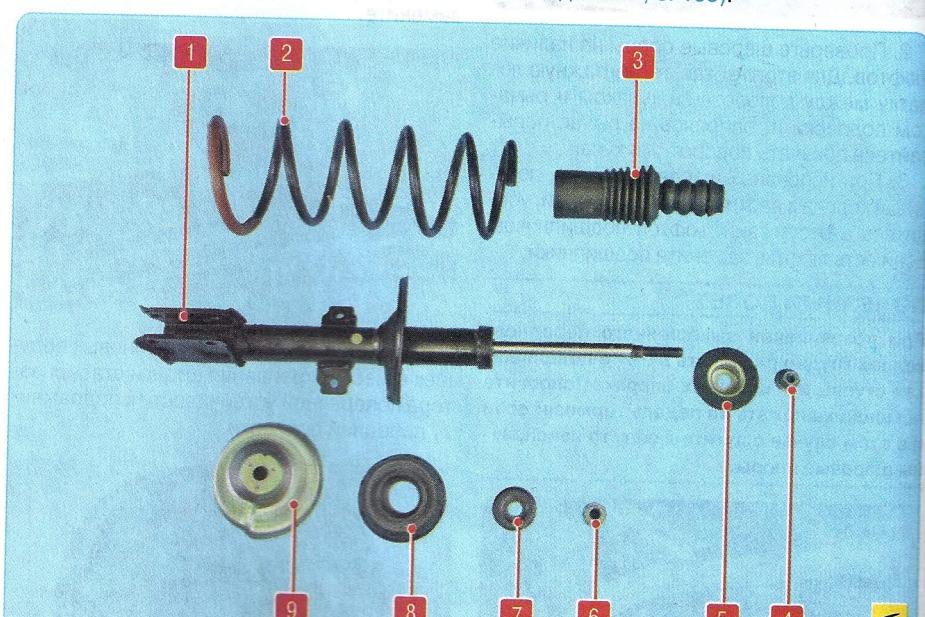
Детали амортизаторной стойки: 1 – амортизатор; 2 – пружина; 3 – буфер сжатия с защитным чехлом; 4 – гайка верхнего крепления амортизаторной стойки; 5 – упорная шайба; 6 – гайка штока амортизатора; 7 – опорный подшипник; 8 – верхняя опора стойки; 9 – верхняя тарелка пружины
